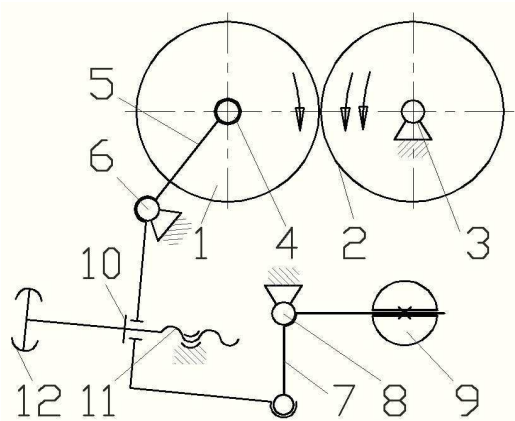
Конструкция установочного механизма с рычагом первого рода
